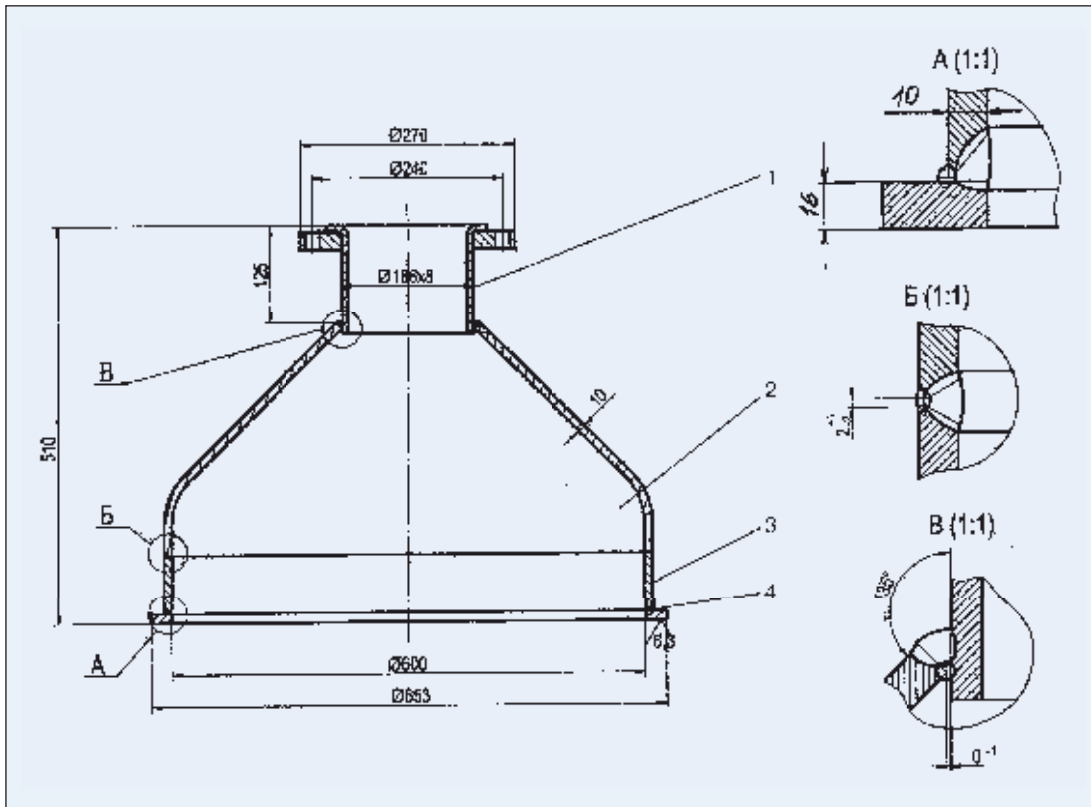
Сварка узлов приемника пара: 1 — патрубок; 2 — коническая обечайка; 3 — цилиндрическая обечайка; 4 — фланец
